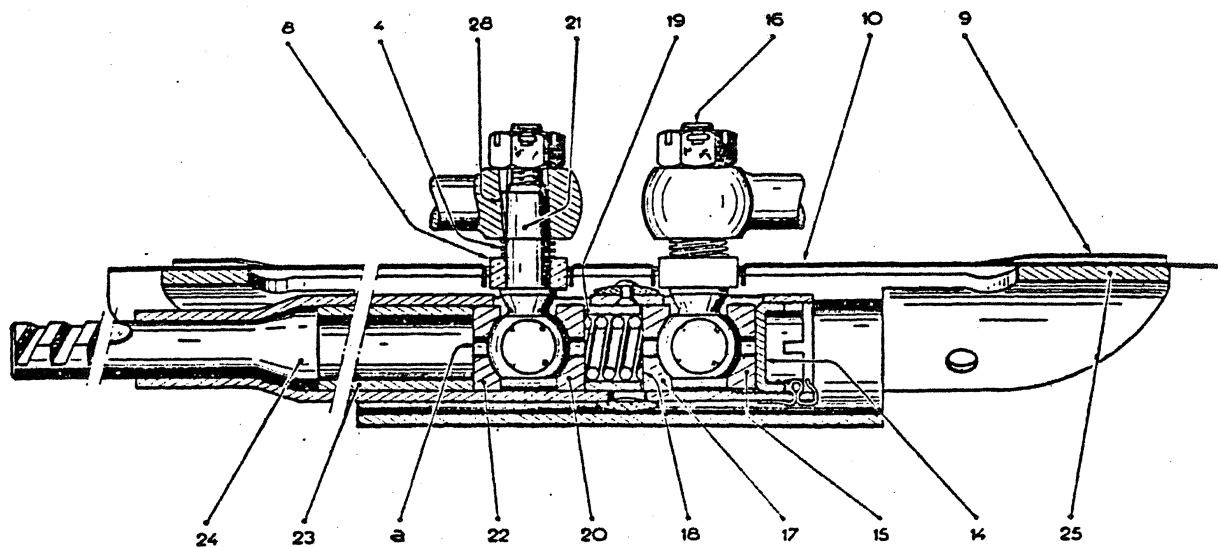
Schnitt durch Zahnstange, Lenkgehäuse und Kugelbolzen
